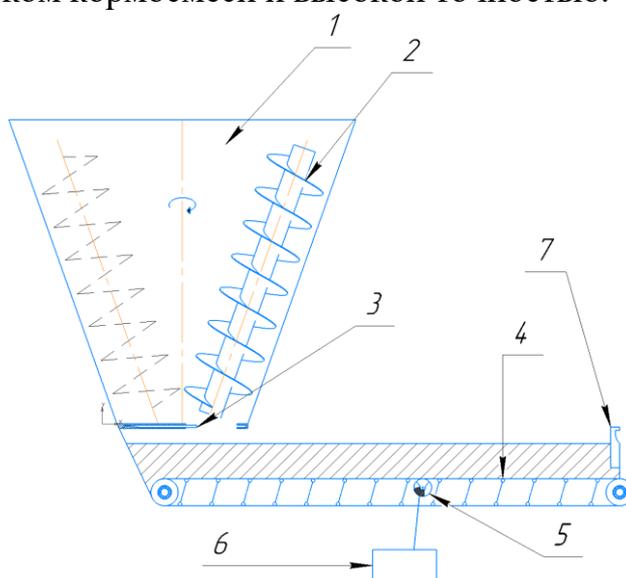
Общий вид дозатора сыпучих кормосмесей:
